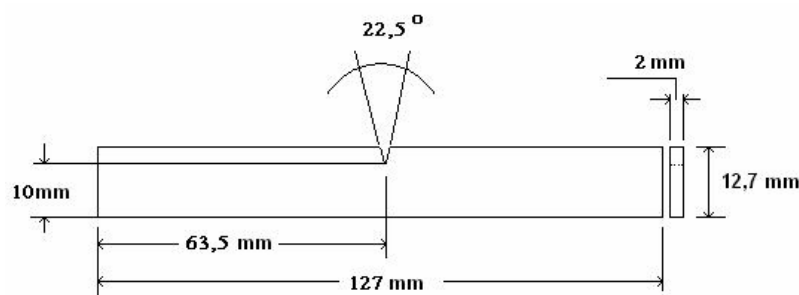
Configuração do corpo de prova de impacto Charpy
